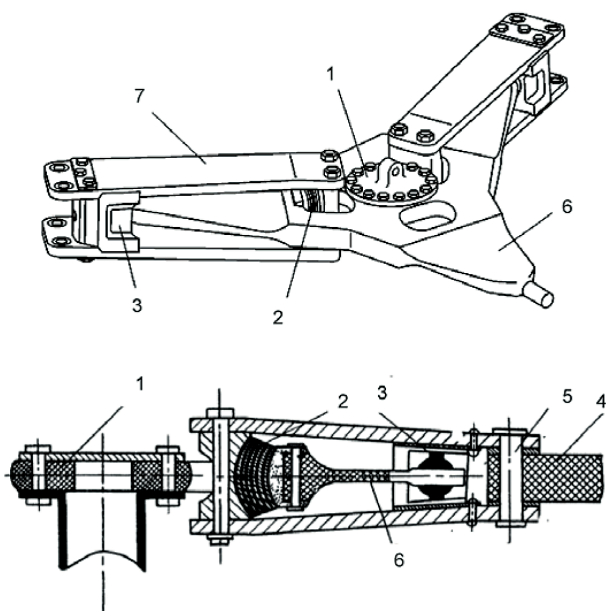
Конструкция втулки с упругим стеклопластиковым элементом типа StarFlex: 1 – корпус втулки; 2 – сферический эластомерный подшипник; 3 – шаровая опора; 4 – лопасть; 5 – болт крепления лопасти; 6 – упругий элемент; 7 – кронштейны
